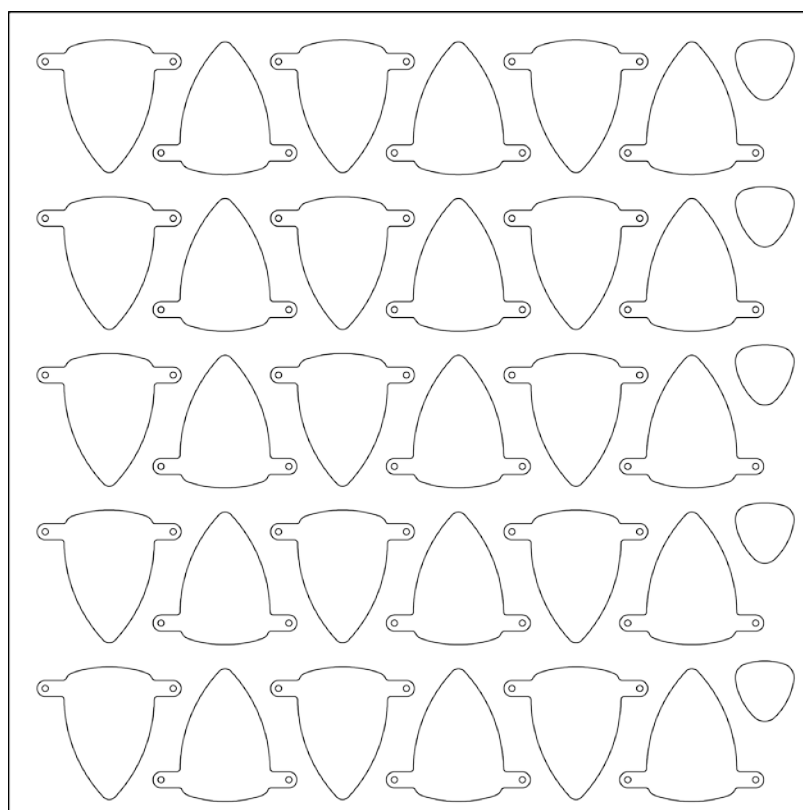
Desenho de corte de peças do conjunto 2 para programação em máquina fresadora
